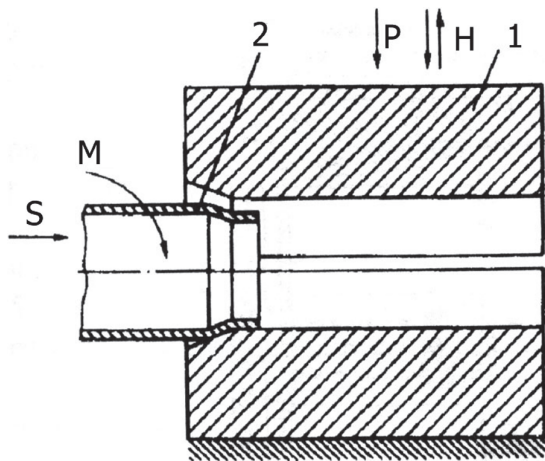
Схема калибровки патрубков с осевой подачей и поворотом на заданный угол за каждый рабочий ход прессы:
